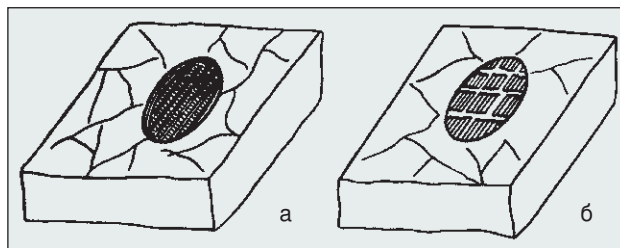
Схема заварки раковин: а — облицовка; б — наплавка
